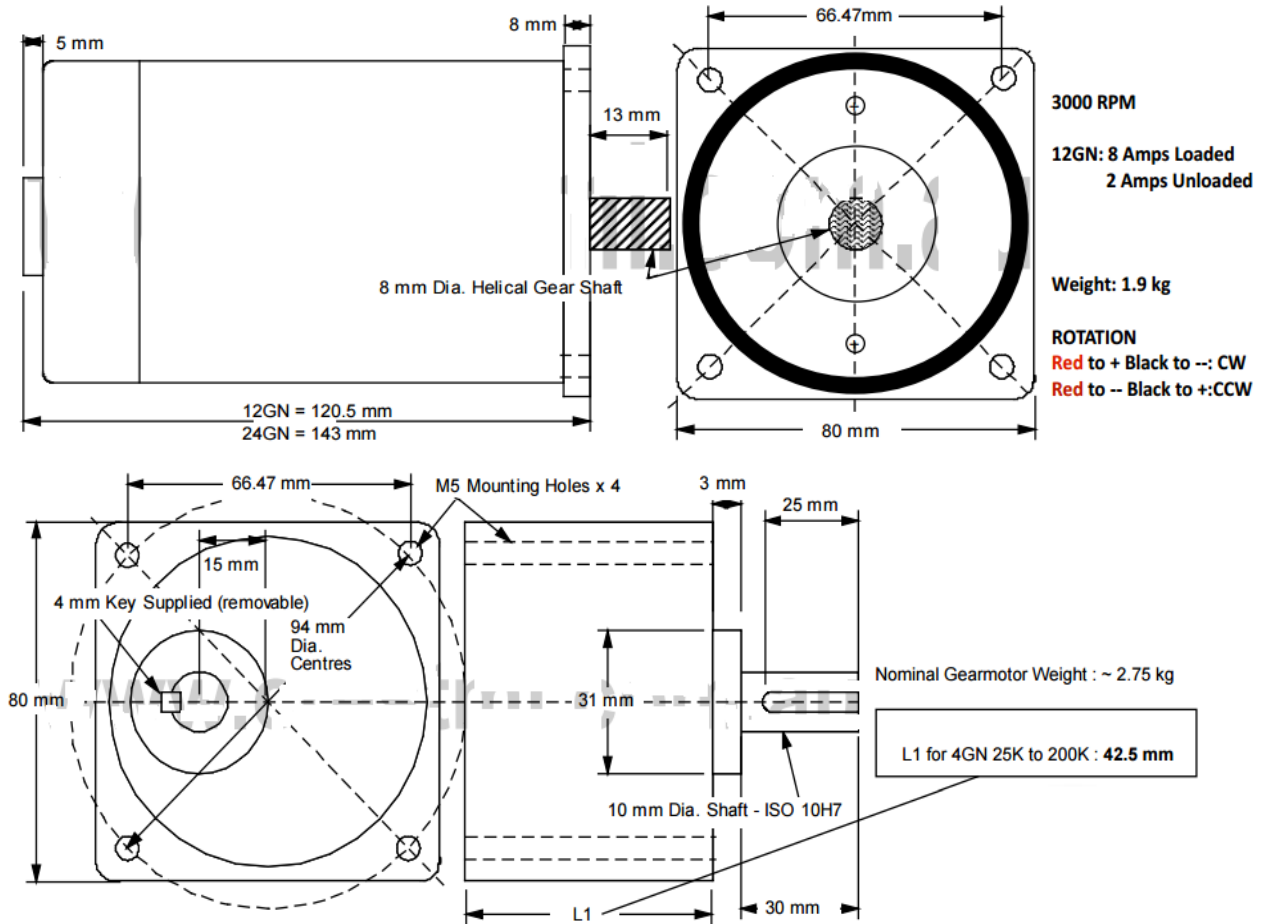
Dimensiones motor Z4D40-12GN-30S con reductor 4GN15K.
